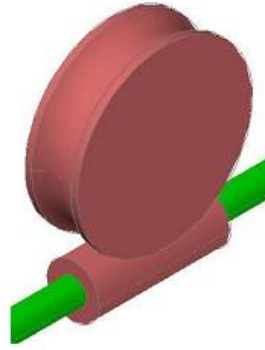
Загальний вигляд черв'ячної передачі на головному валу для приводу контролера
